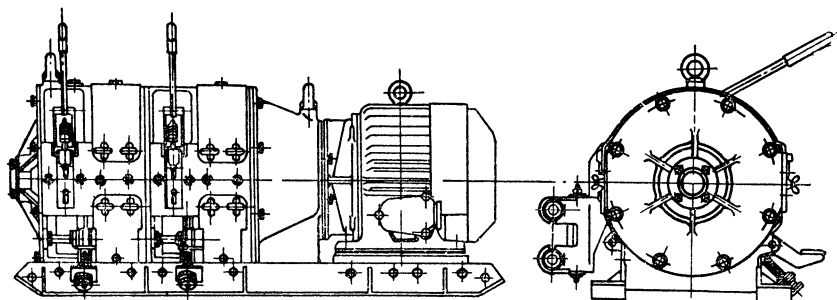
Общий вид скреперной лебедки 2ЛСЭ-28
